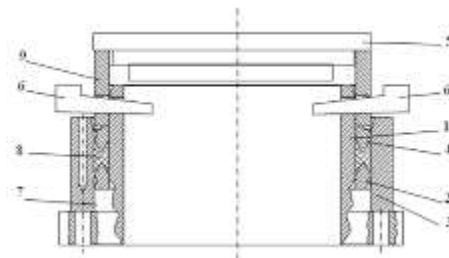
Уплотнительные манжеты из фторопласта – 4 для гидроцилиндров подвески автомобилей БЕЛаз, выпускаемые промышленностью (1, 2) и манжеты, полученные объемной штамповкой из кольцевых заготовок (3, 4)
